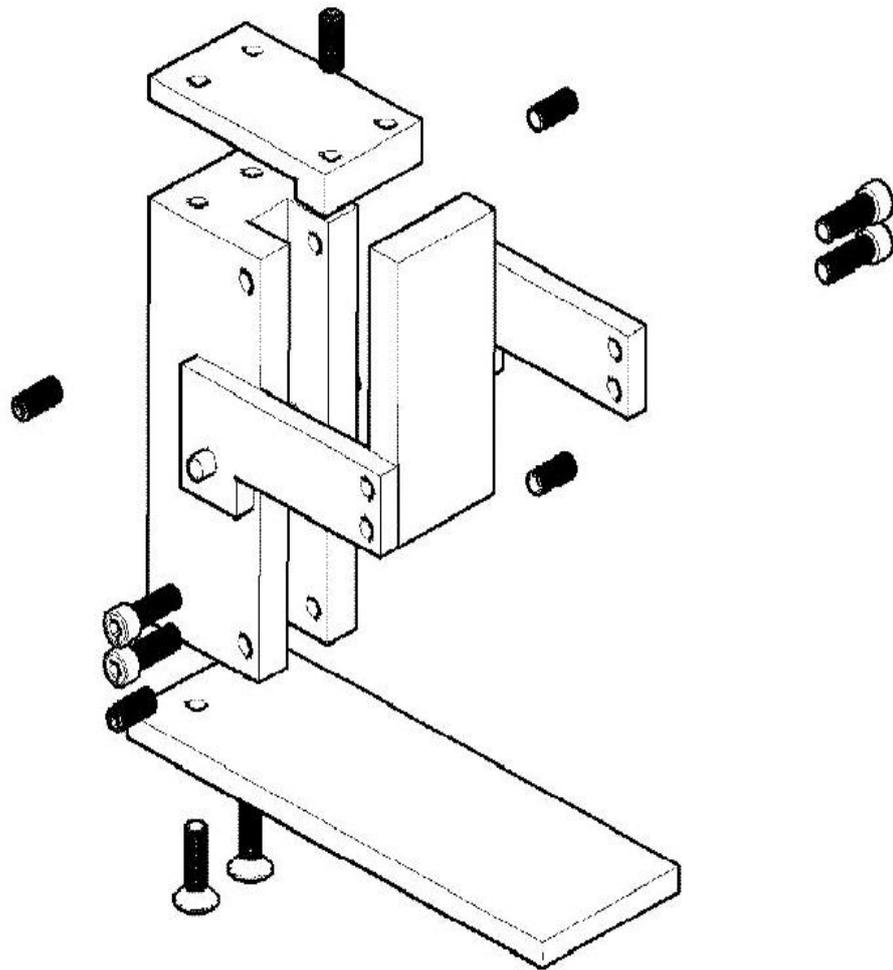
Mesin uji tekan TARNO GROCKI
